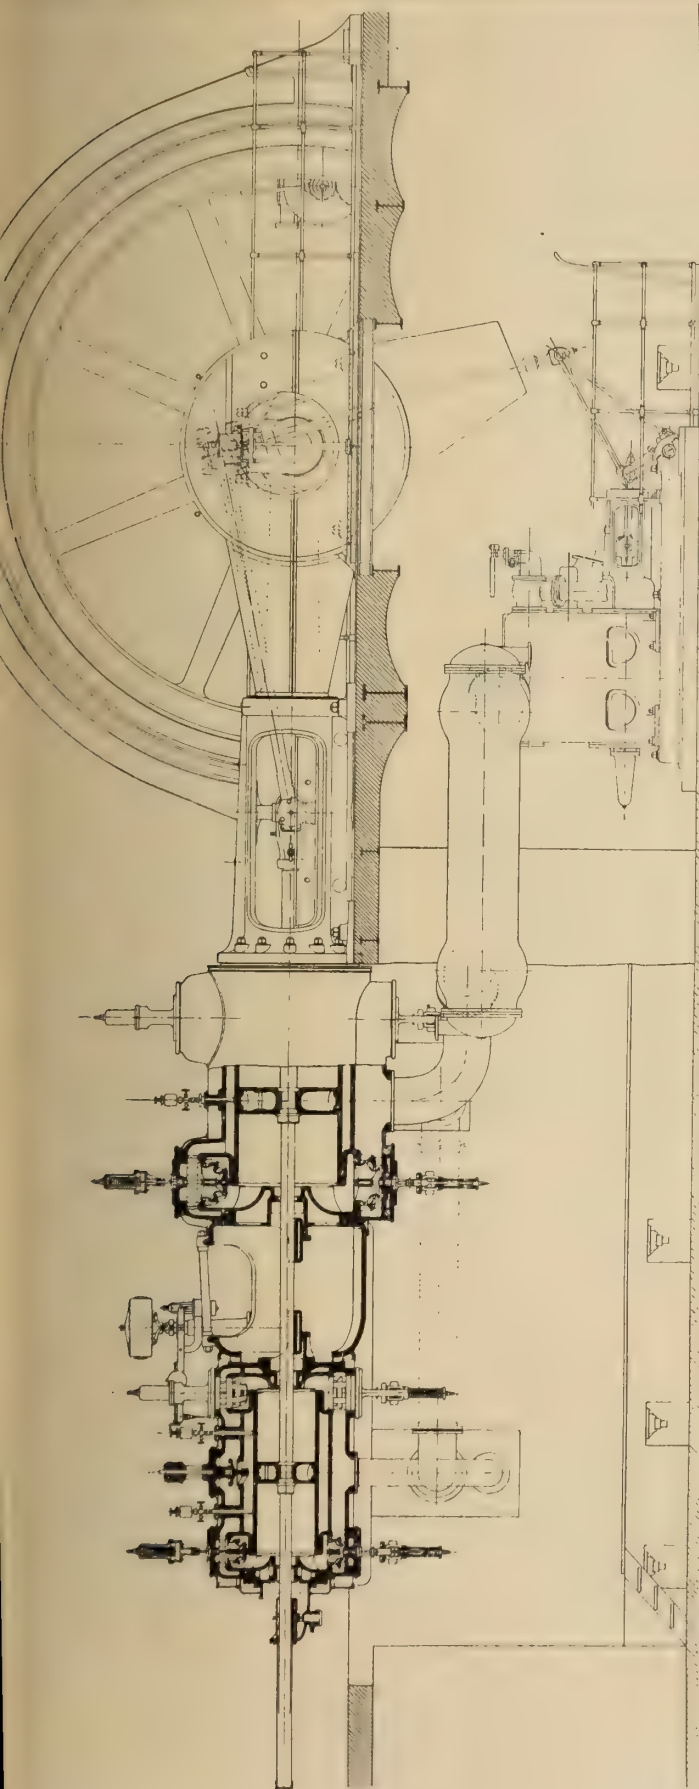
Längsschnitt durch den Hochdruckzylinder einer Generatorenmaschine.
